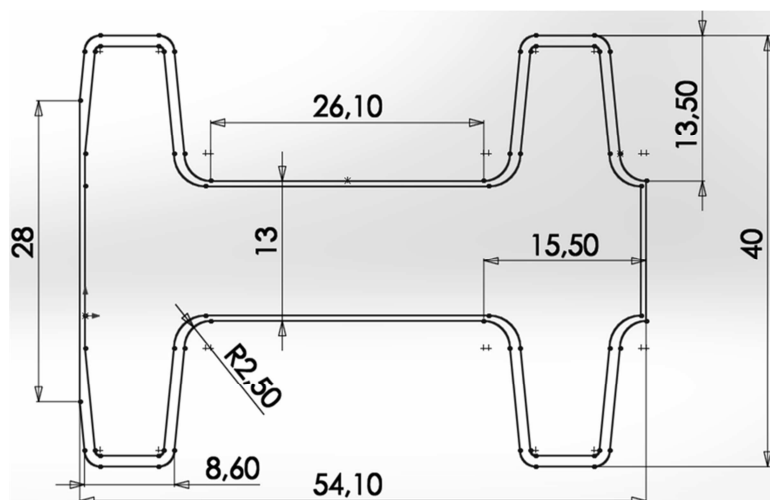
Розгортка поковки з припуском з розмірами (вигляд зверху)
